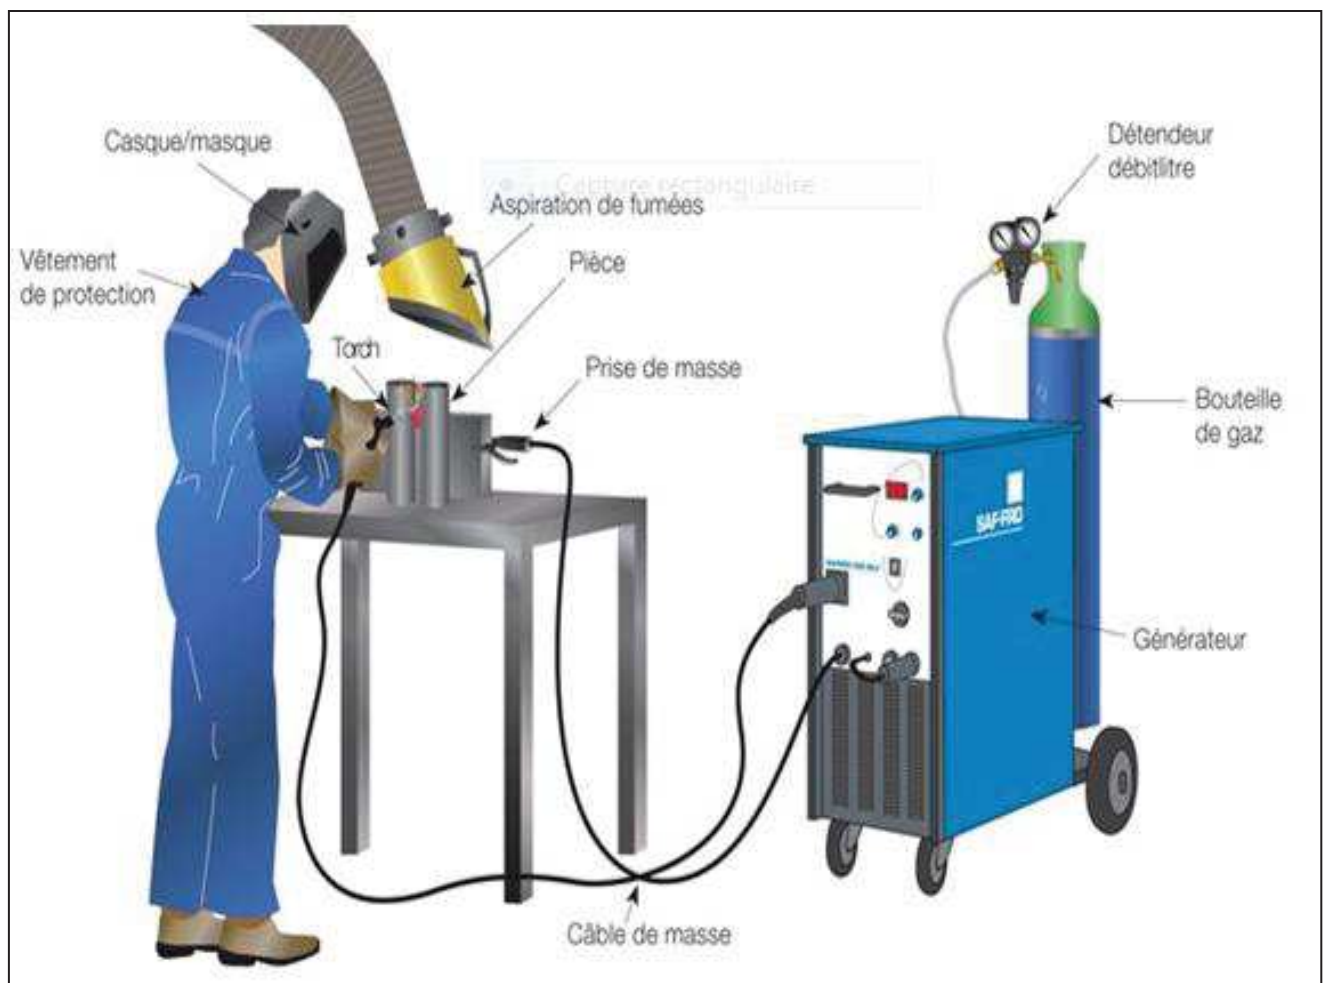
Schéma d'installation manuel pour soudage MIG-MAG [2]
